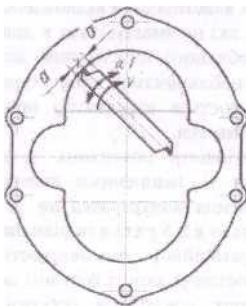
Напрямок обертання різця та крутильних коливань деталі при вібраційному розточуванні колодязя корпусу насоса підживлення: а - амплітуда коливань, f - частота коливань, V - напрям обертання різця.
